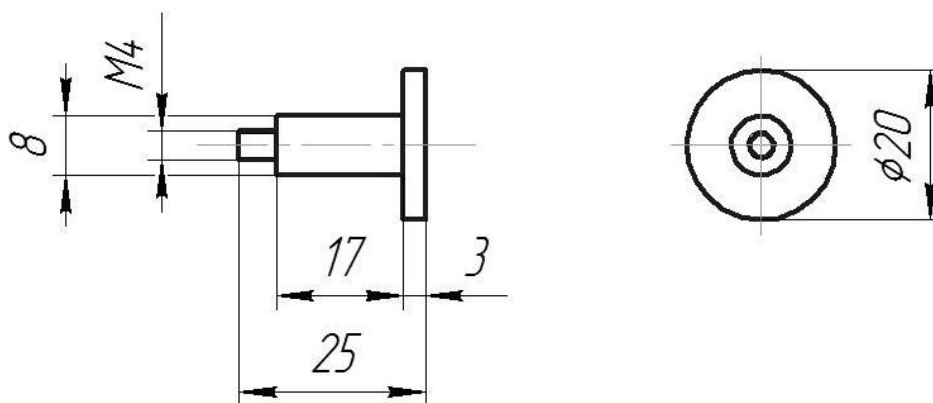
Габаритные размеры ручки для выемки блока
